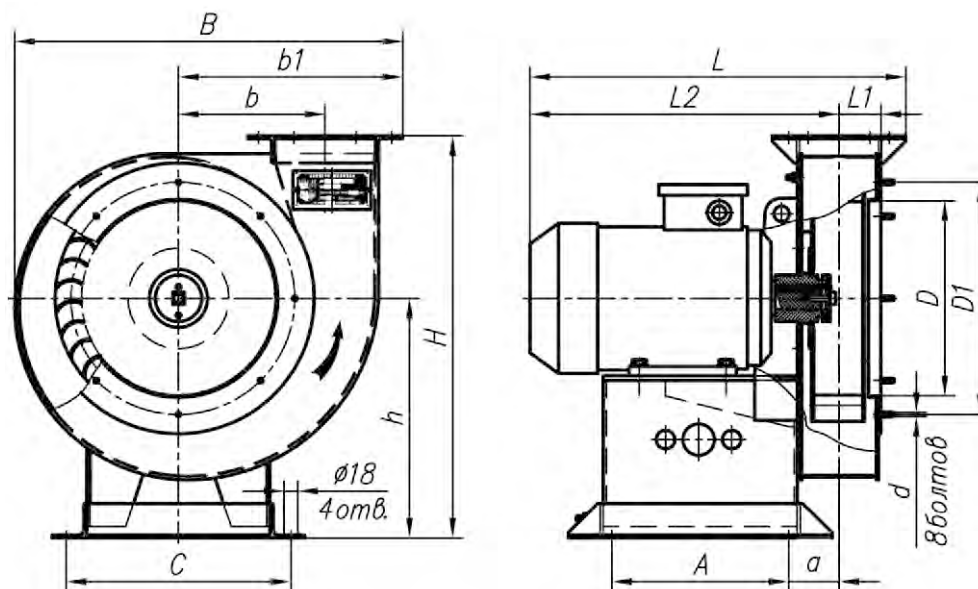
Положение корпуса вентилятора ВР 12-26.
